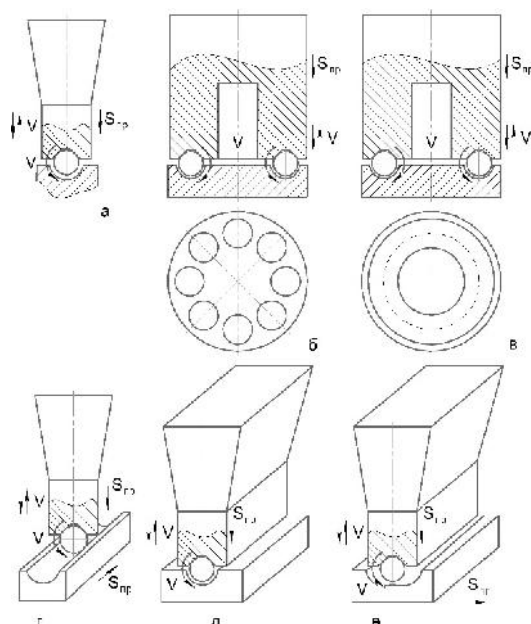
Кинематические схемы размерной ультразвуковой обработки незакрепленным инструментом [1].
